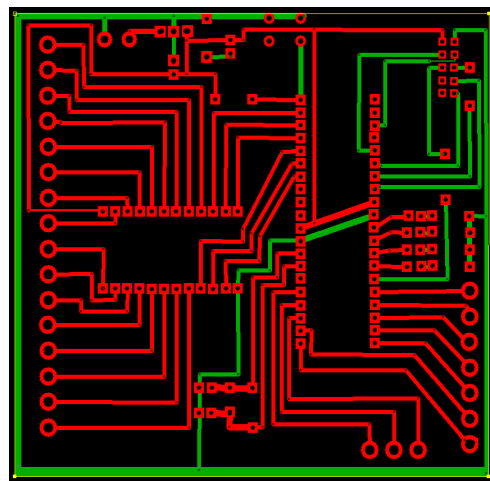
Placa de circuito impresso do dispositivo concentrador.
